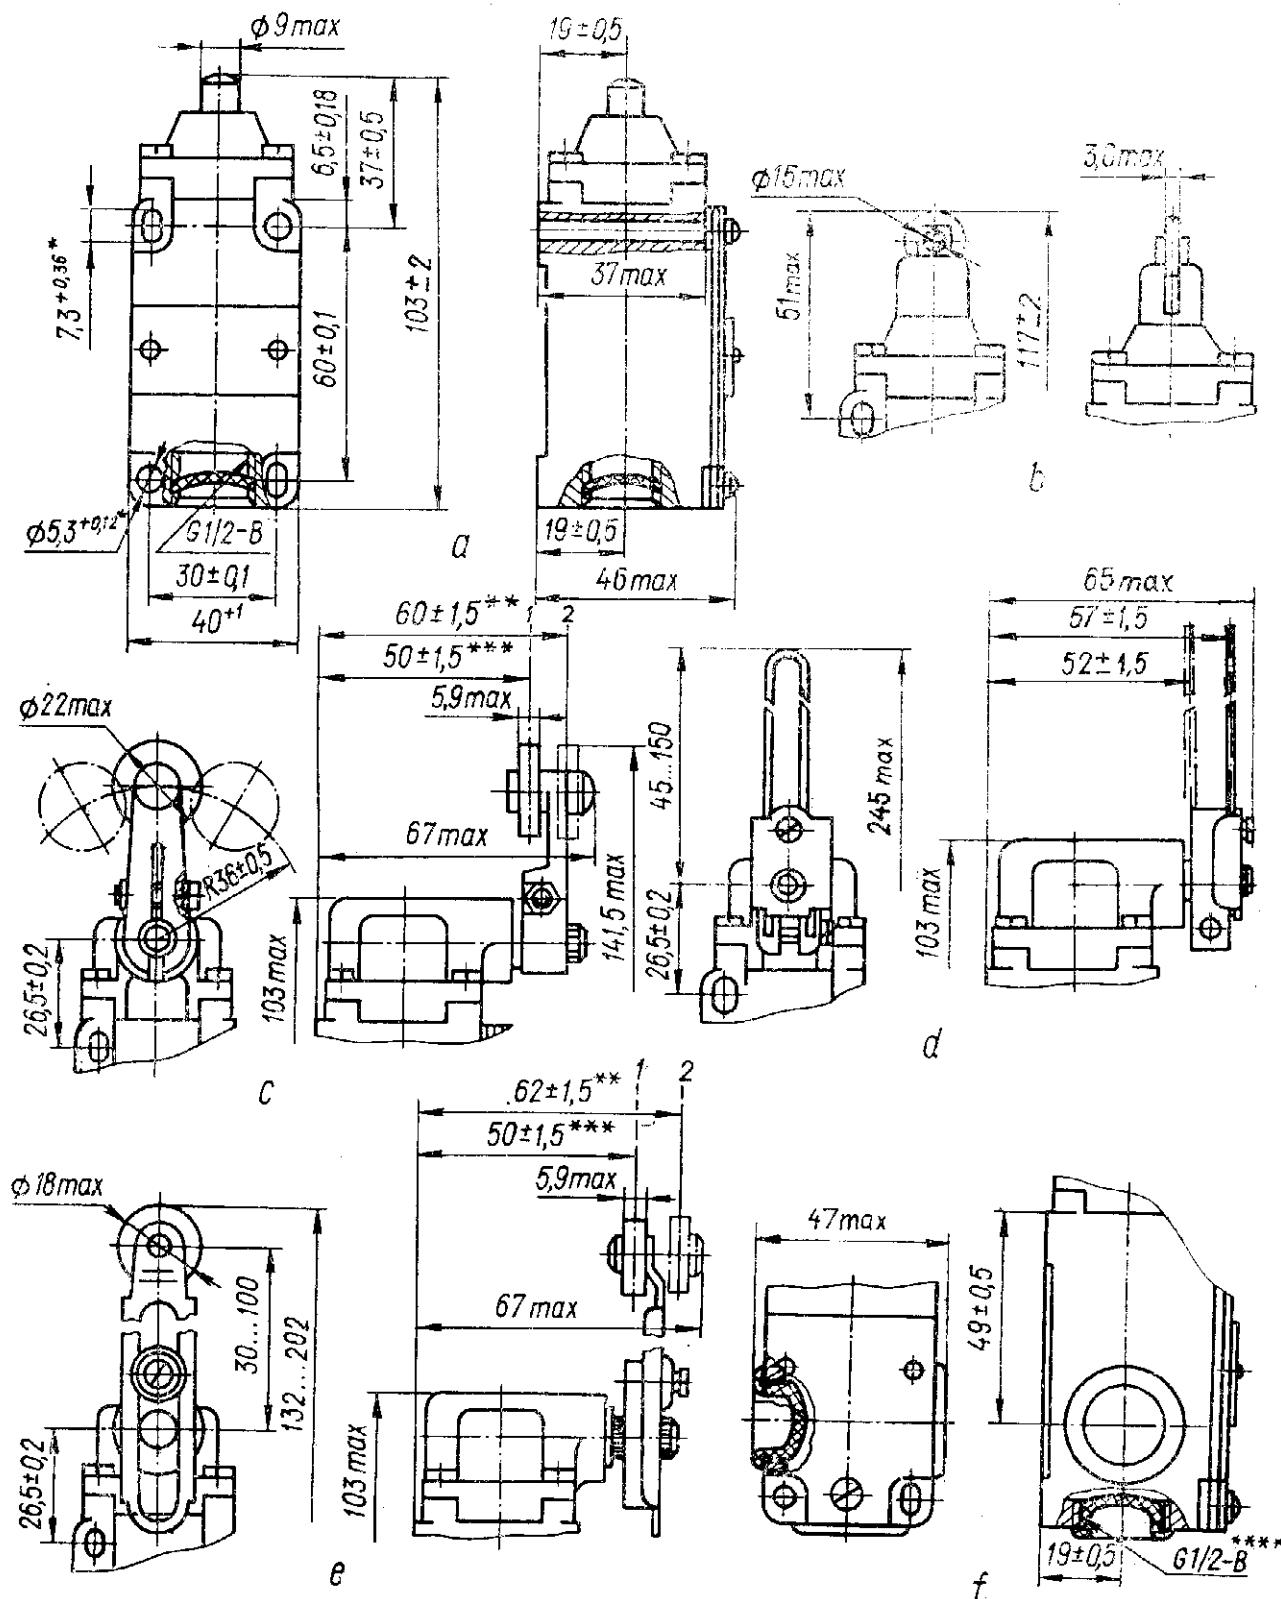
Габаритные, установочные, присоединительные размеры выключателей:
